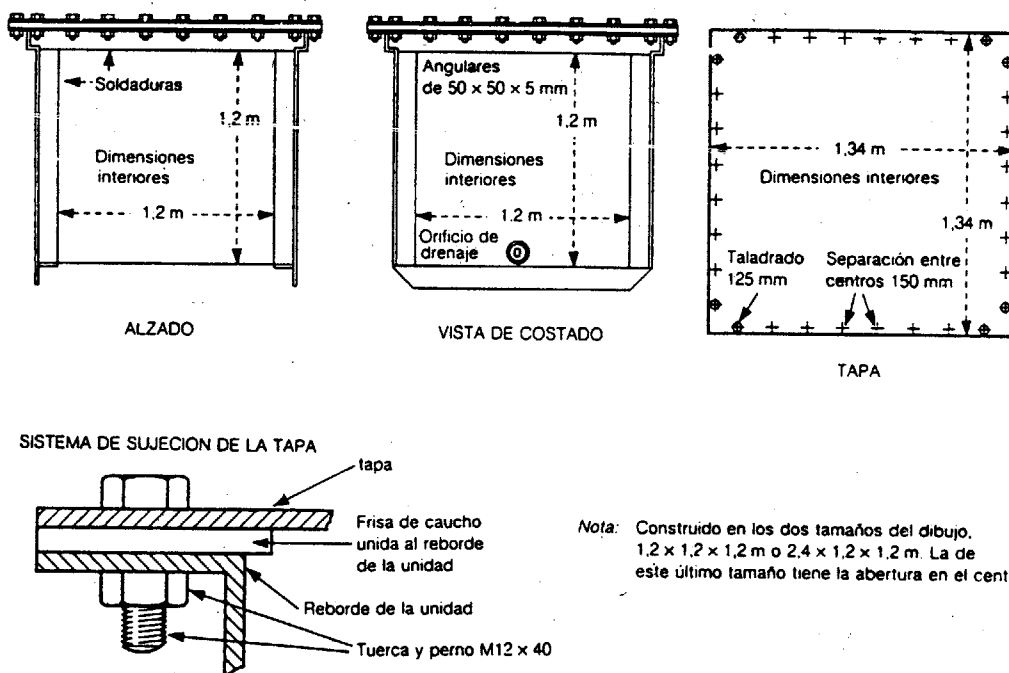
Ejemplo de pañol de explosivos portátil de acero, de elementos soldados o empernados
